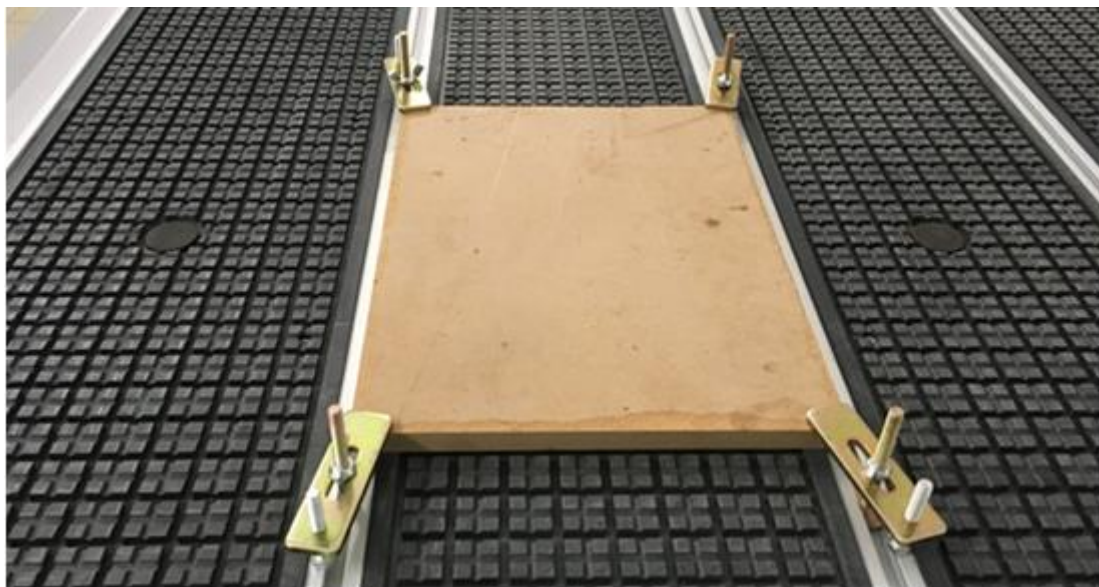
Крепление заготовок с помощью прижимных струбцин
